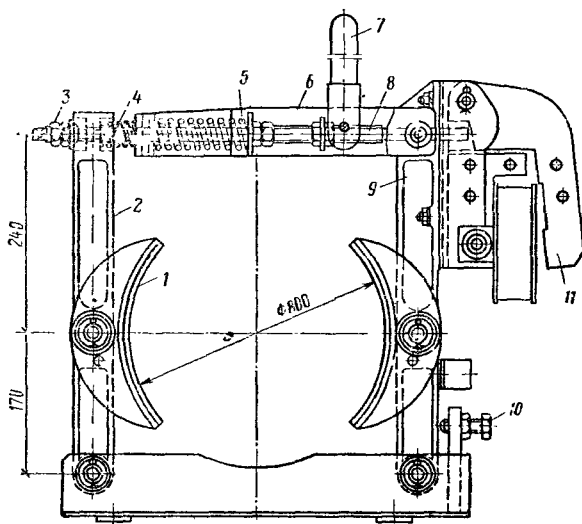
Двухколодочный пружинный электромагнитный тормоз
